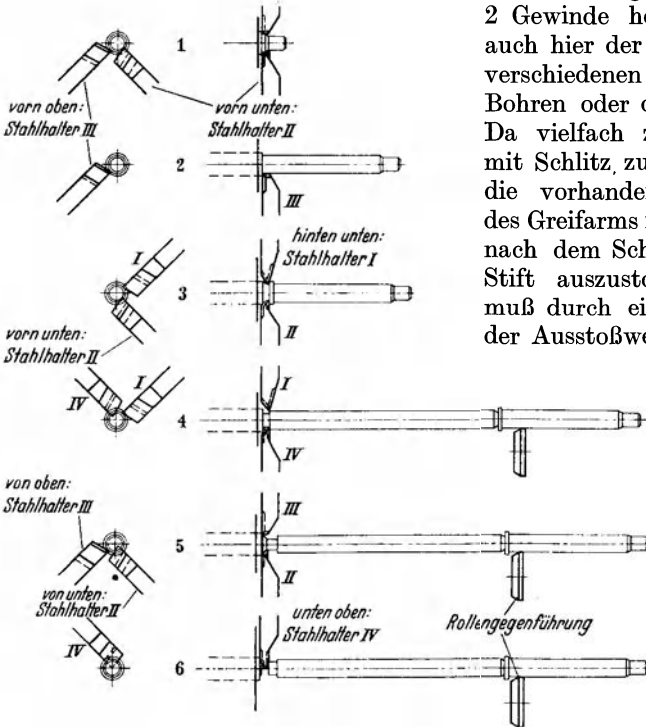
Bearbeitung einer Motorenwelle von 230 mm Länge auf Automaten nach Abb. 46.
